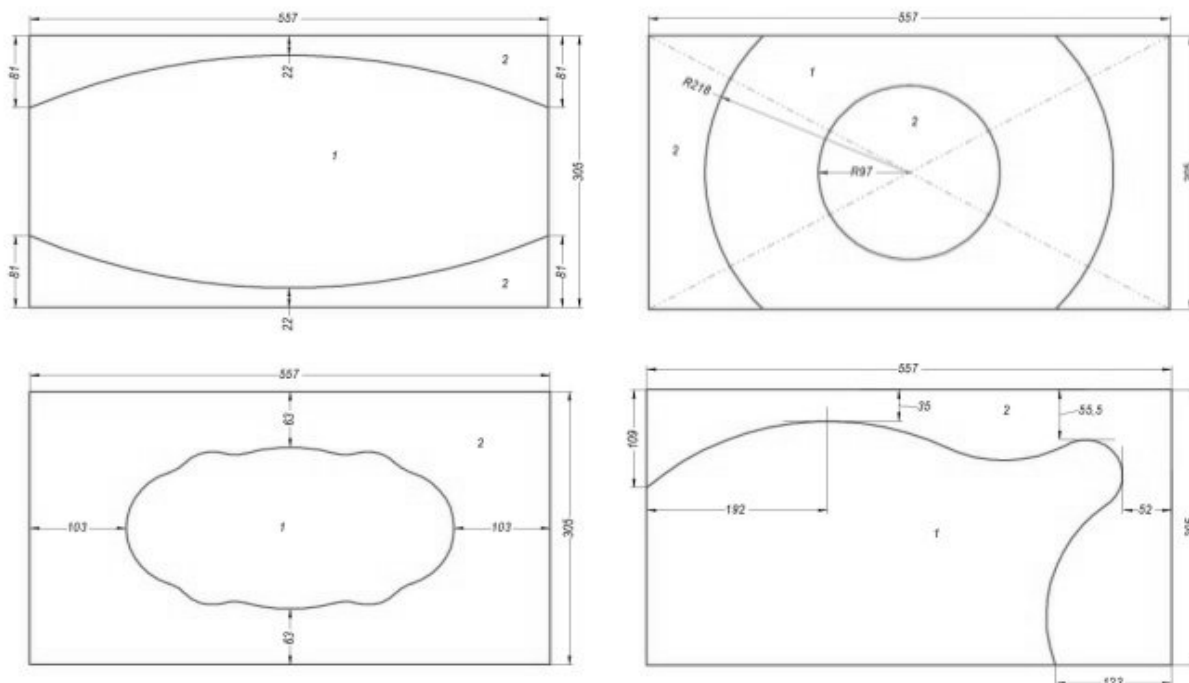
Примеры эскизов для изготовления заказных конструкций
